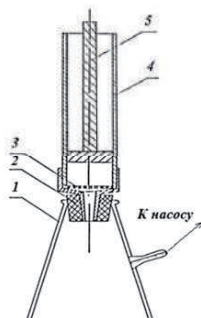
Оснастка для изготовления изделий цилиндрической формы.
